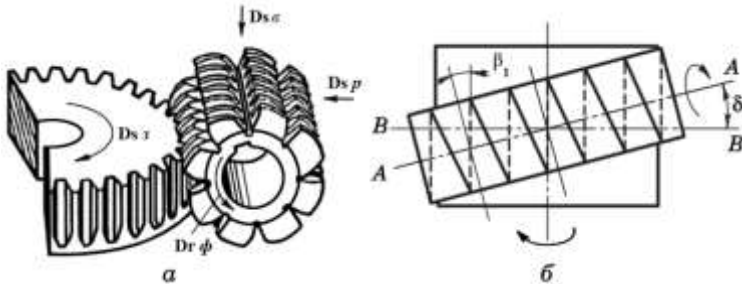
Нарізування зубців коліс черв'ячною фрезою:
